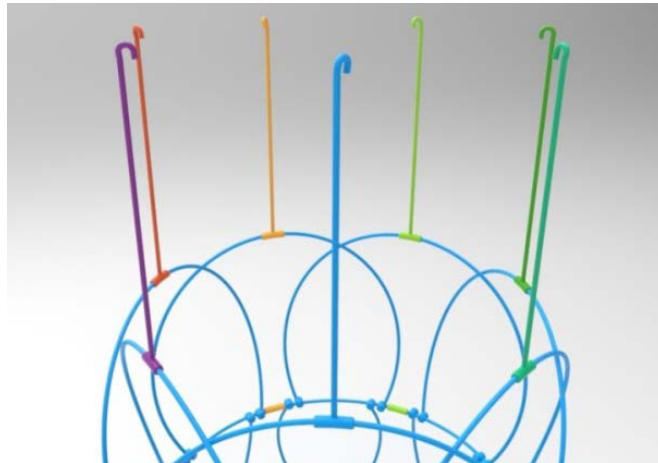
Detalle de las varillas situadas en la zona superior de la estructura.
